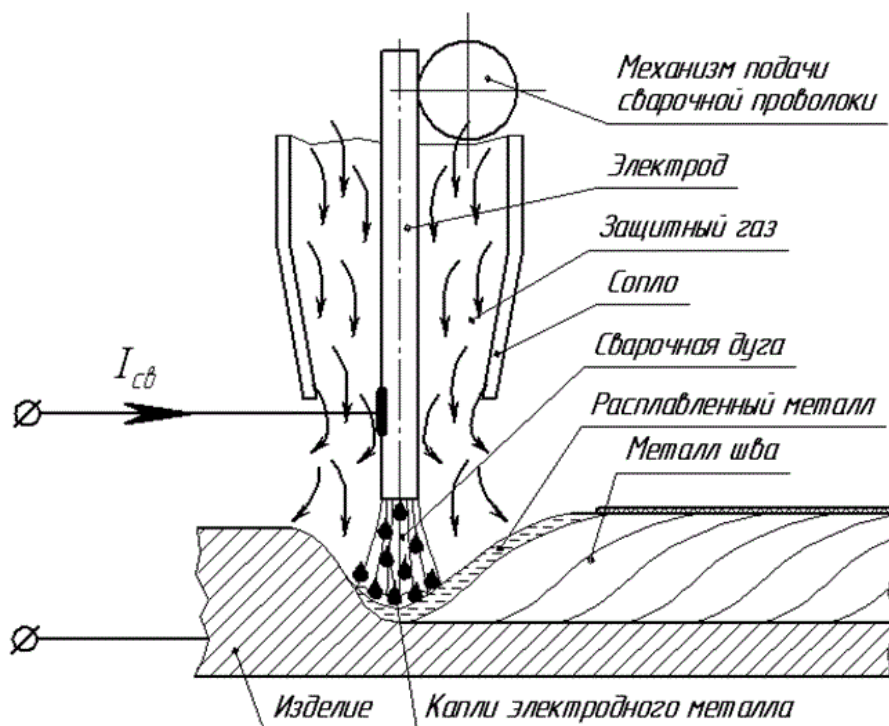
Схема процесса сварки в защитном газе плавящимся электродом
